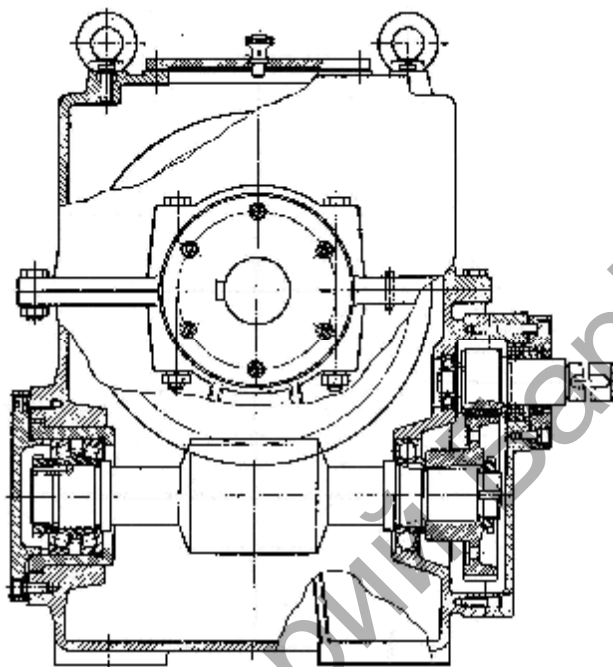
Цилиндрическо-червячный редуктор [18]
